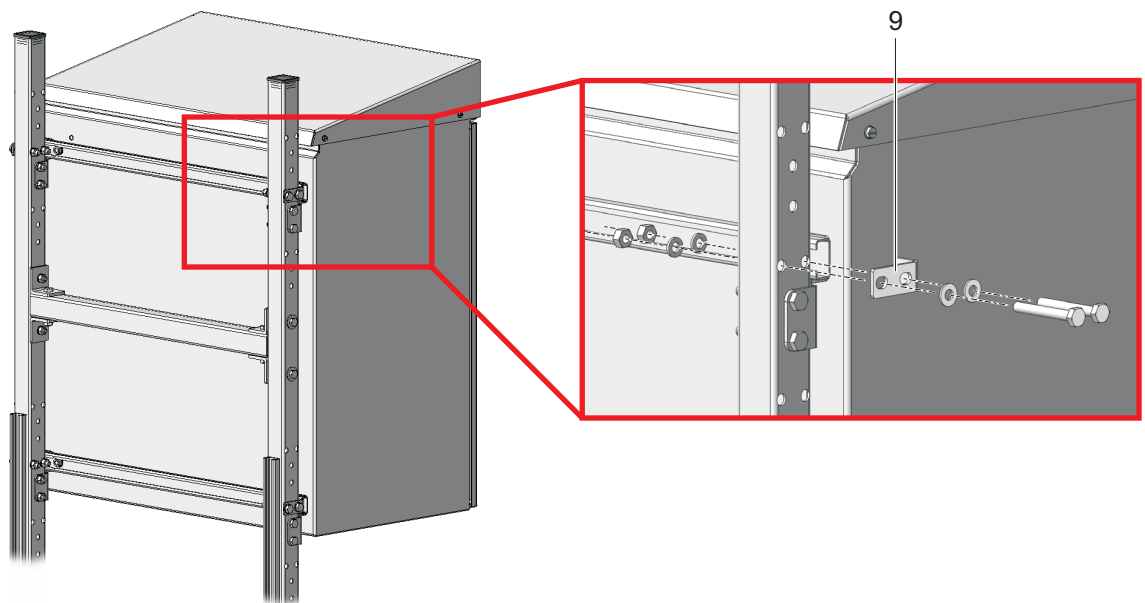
Gehäuse befestigen (rechts: Detailansicht)
